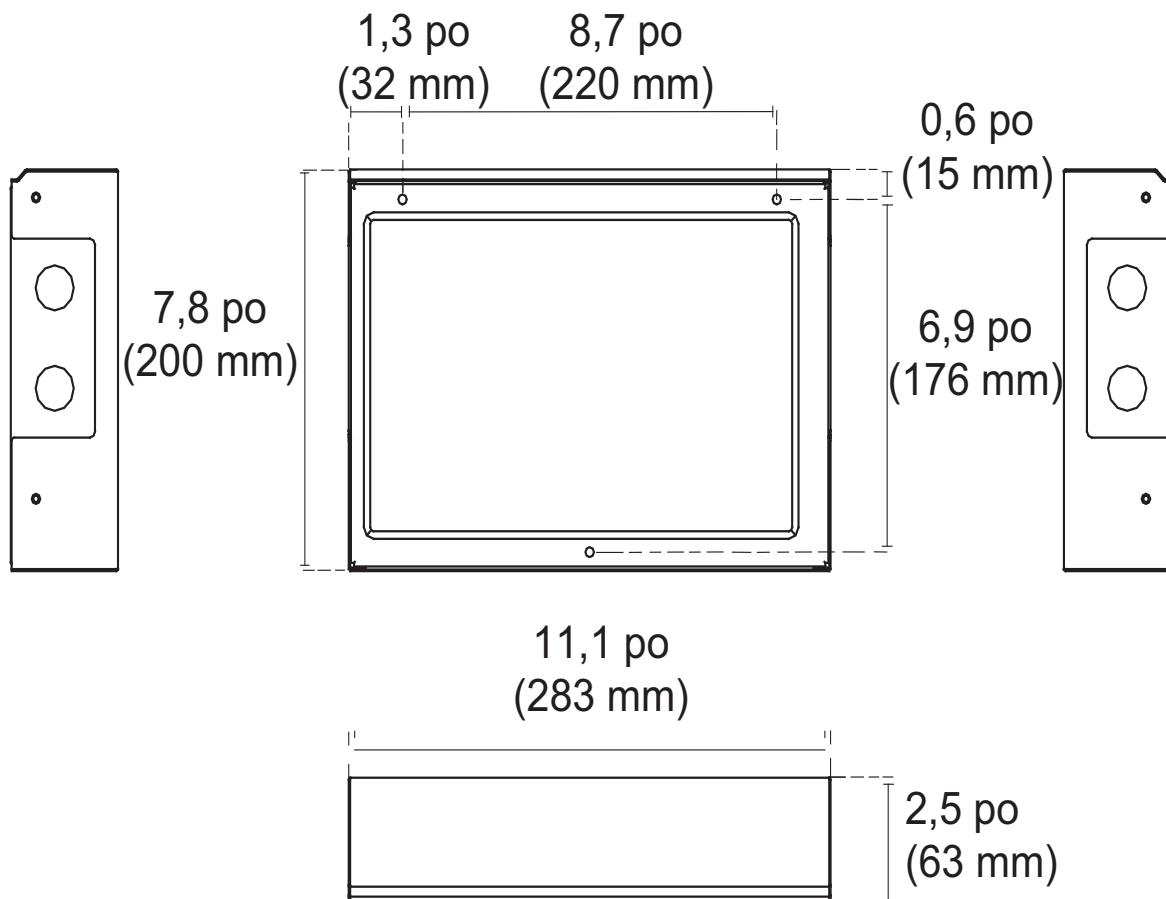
Dimensions du boîtier de l'interface 24 V
